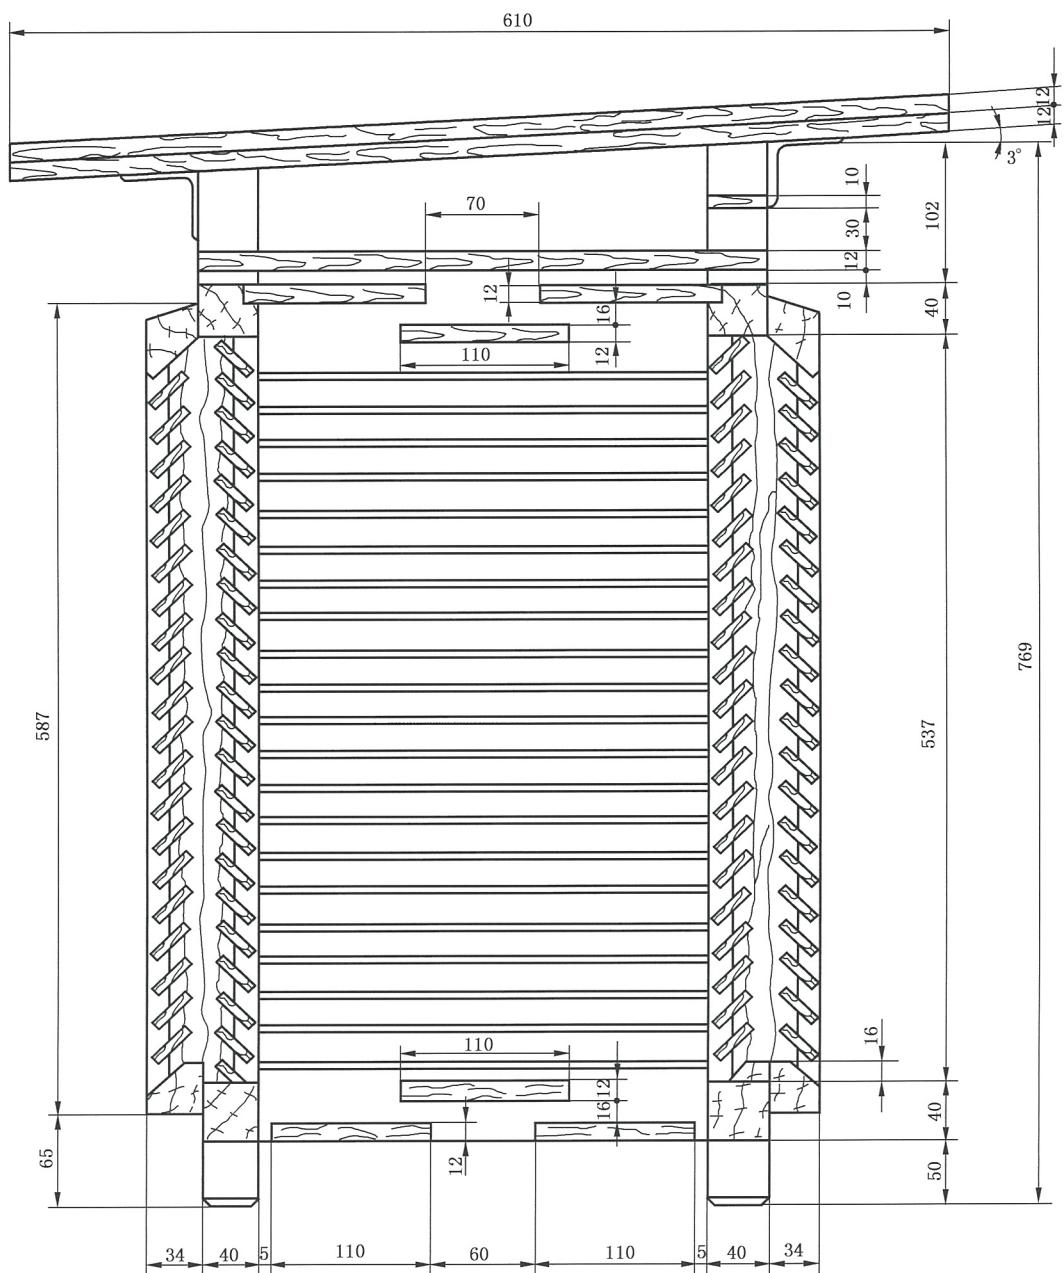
木制小百叶箱侧面剖视图结构参考尺寸
